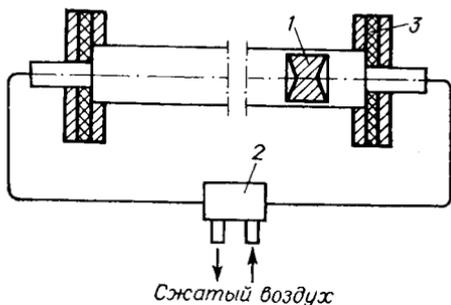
Приспособление для пневмомеханической чистки труб:
